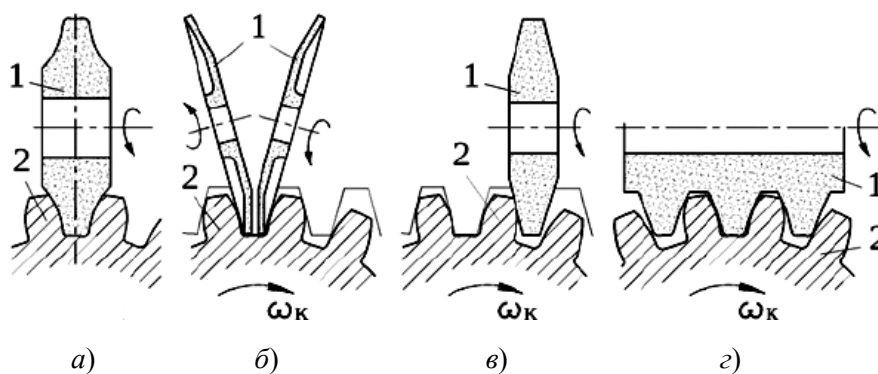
Методы шлифования профиля зубьев цилиндрических колес:
